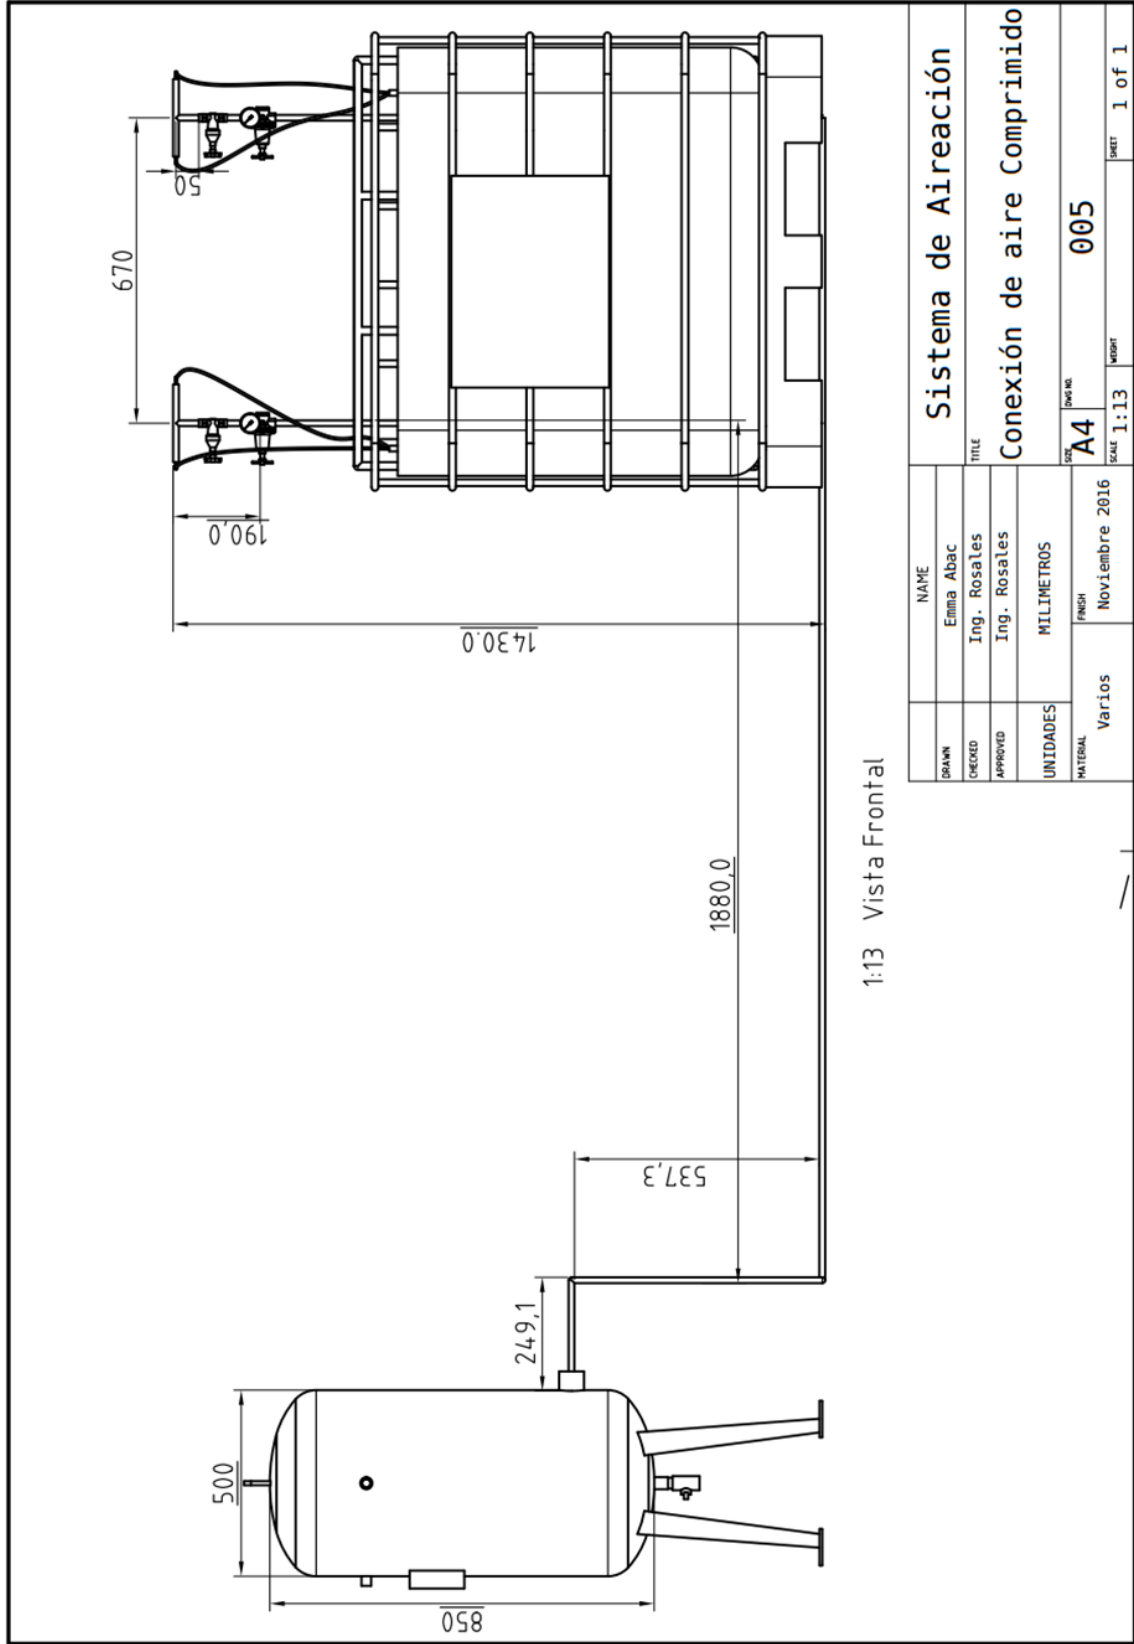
Plano de vista de planta del sistema de aireación de la planta de tratamiento de aguas residuales a escala planta piloto.
